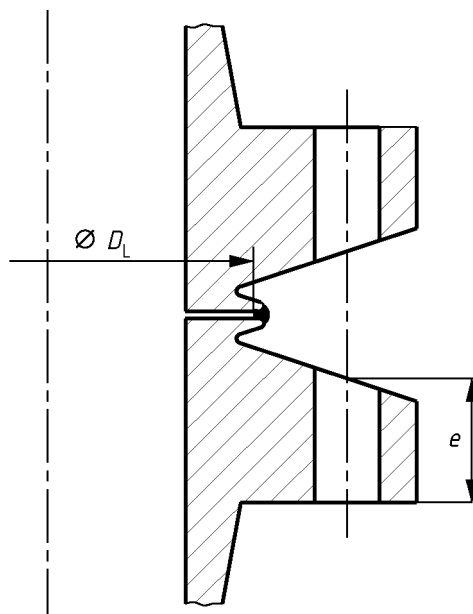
Brida con soldadura de cierre
